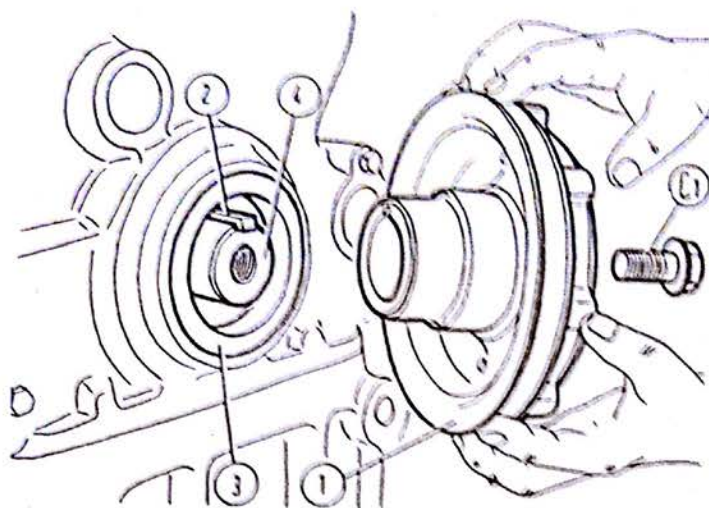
/28 - Dépose de la poulie (1) de vilebrequin (4). C1. Vis de fixation de la poulie - 2. Clavette - 3. Joint à lèvres.
